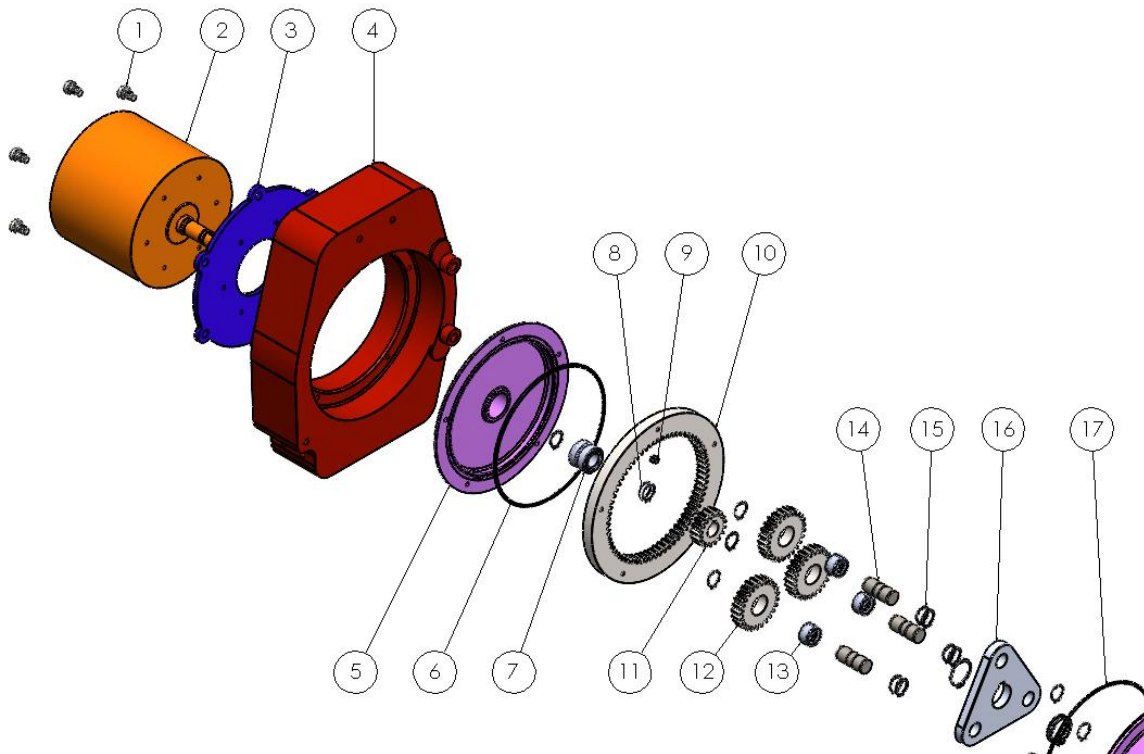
Vista explosionada del sistema de transmisión propuesto (Parte A).
